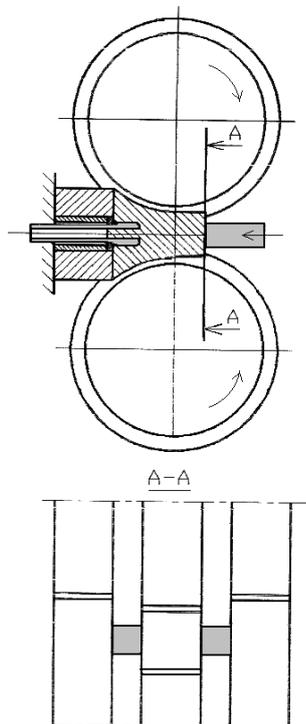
Универсальное устройство для получения пресс-изделий различной формы
